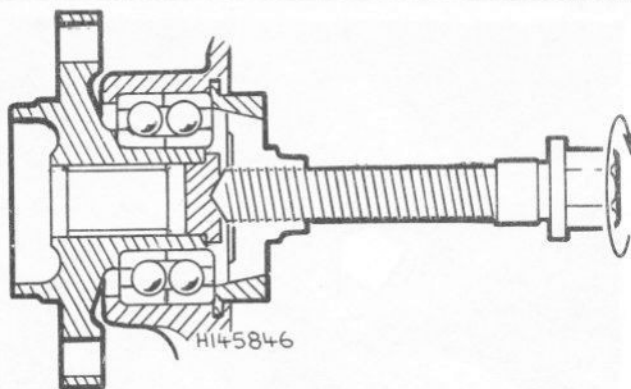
Dépose du moyeu avant à l'aide de l'outil Peugeot 80613B (Sec 7)
